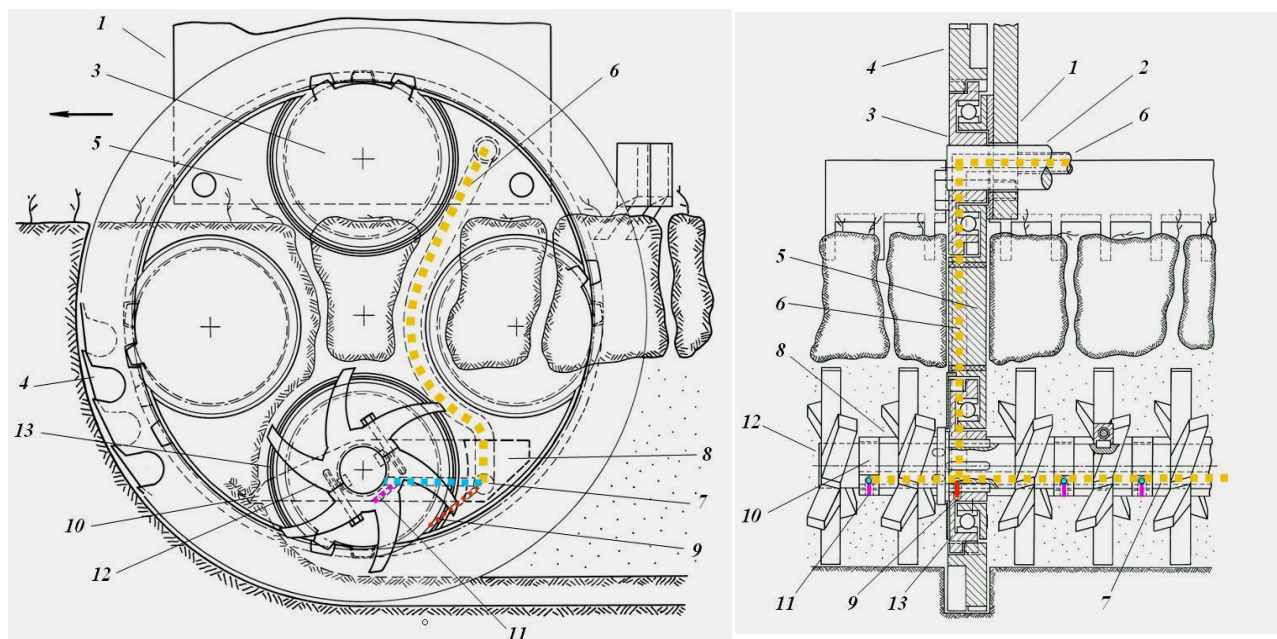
Устройство для внесения вещества в процессе фрезерного внутривнутреннего рыхления.
